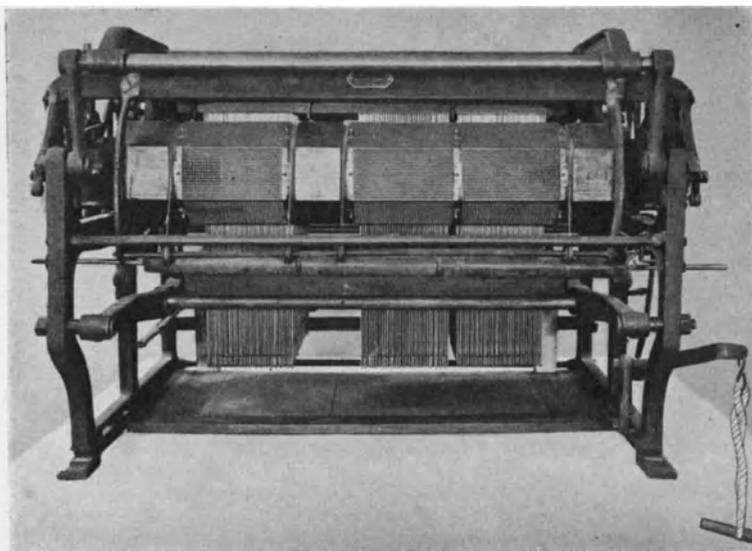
Zweikartige Hoch-, Tief- und Schrägfachmaschine der Firma Maschinenfabrik Karl Zangs, A.-G., Krefeld, ältere Ausführung von der Prismenseite.
